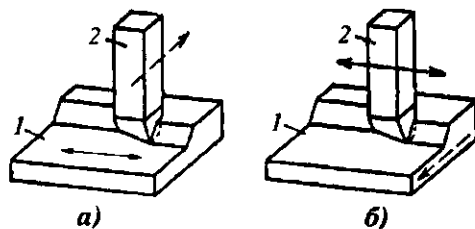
Схемы основных движений при строгании: а – продольном; б – поперечном; 1 – обрабатываемая деталь; 2 – резец; —> — главное движение резания; —> — движение подачи
